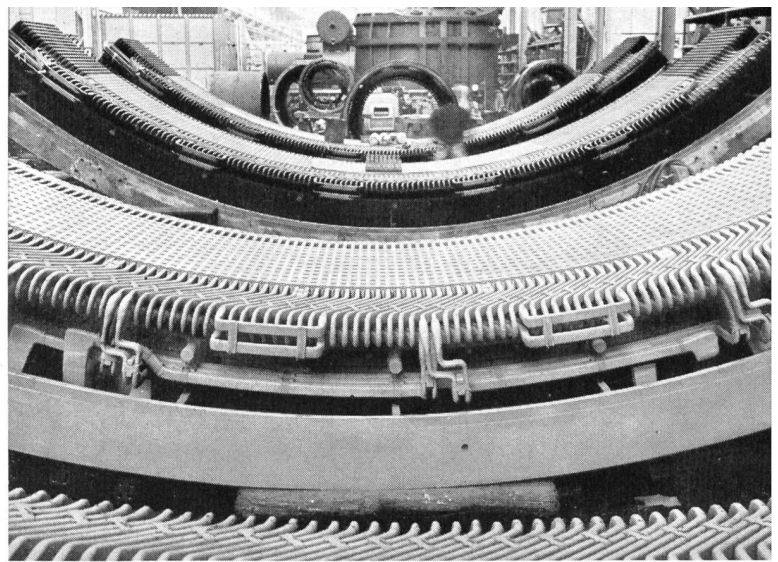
Disposition en «tambour» des têtes de bobines sur un stator en plusieurs parties
